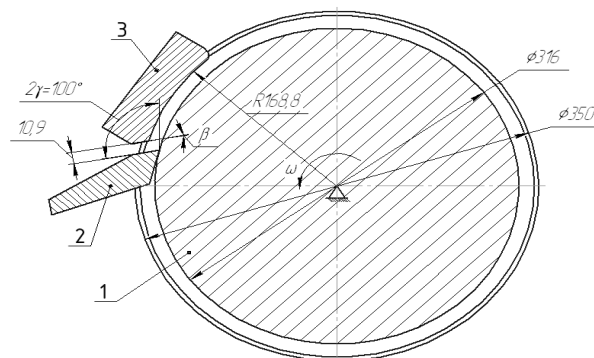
Схема инструмента РКУП-К для прессования заготовок прямоугольного сечения: 1 – ротор; 2 – упор; 3 – прижим
